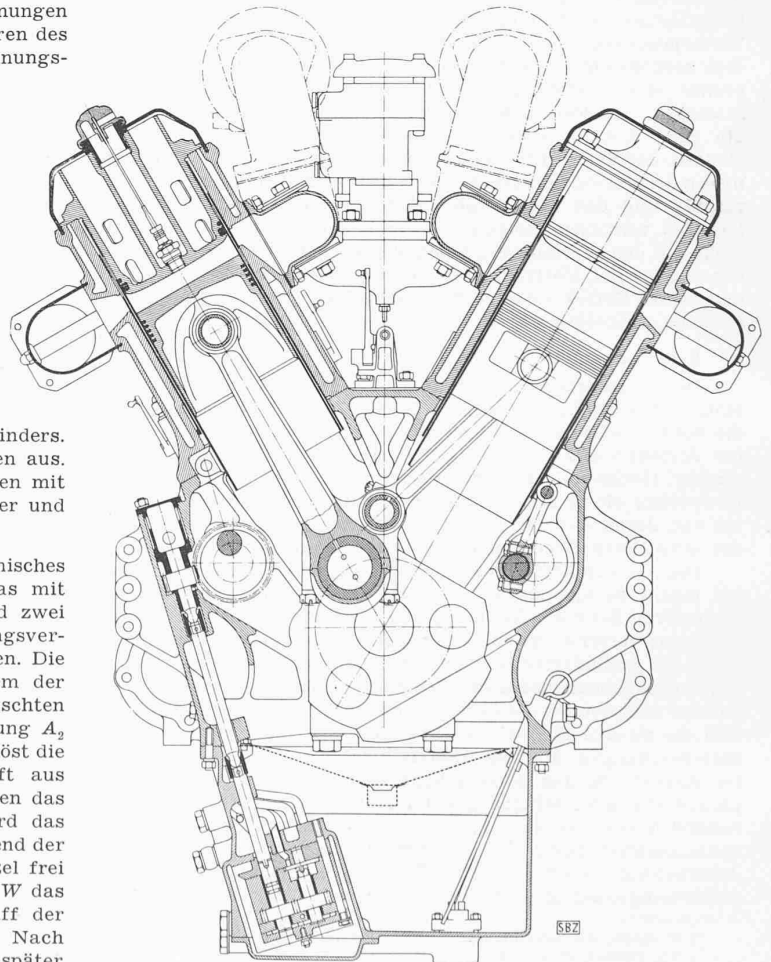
Ventilloser Zwölf-Zylinder Holzkohlengas-Motor Bauart Panhard-Levassor für 270 PS. — Schnitt 1:8
